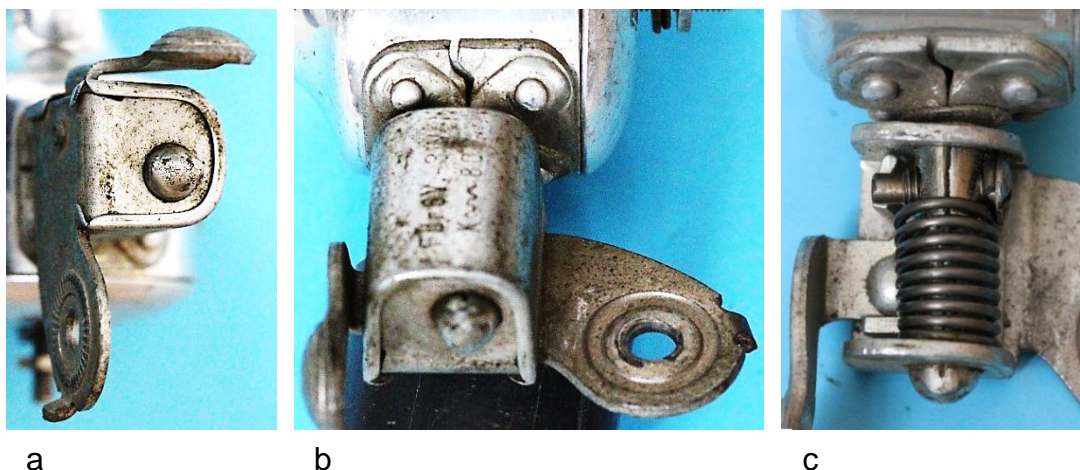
Kippvorrichtung: a) Geschlossene Stirnseite des Drehbolzens, b) Geteilter Flansch, c) Ansicht des gefalteten Drehbolzens
